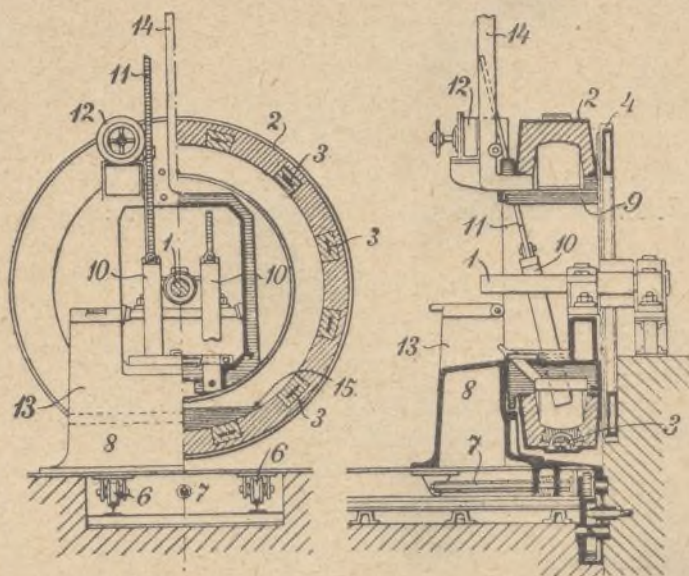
Corte vertical del horno, perpendicularmente al eje.
